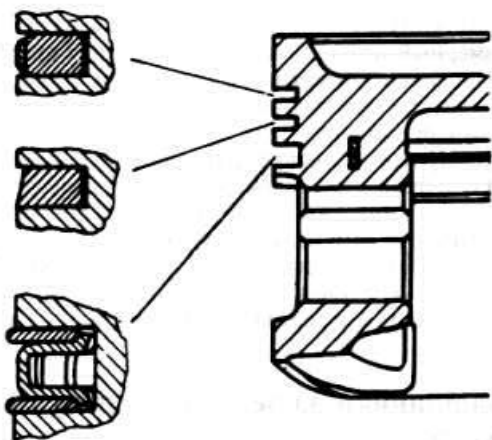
Правильное расположение поршневых колец — для всех двигателей)
